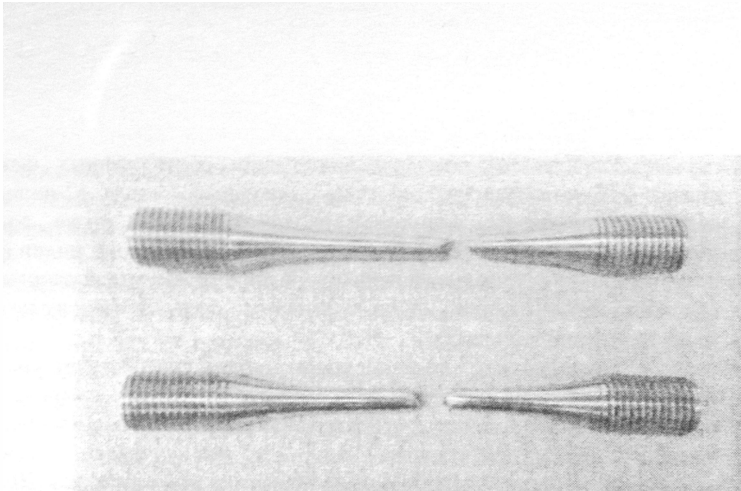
Вид изломов образцов, полученных из шатунов (вверху) и штампованных заготовок (внизу).
